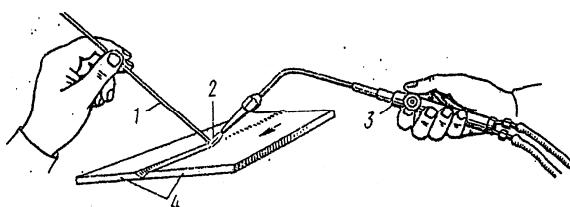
Ручная газовая сварка: 1 – присадочная проволока;
